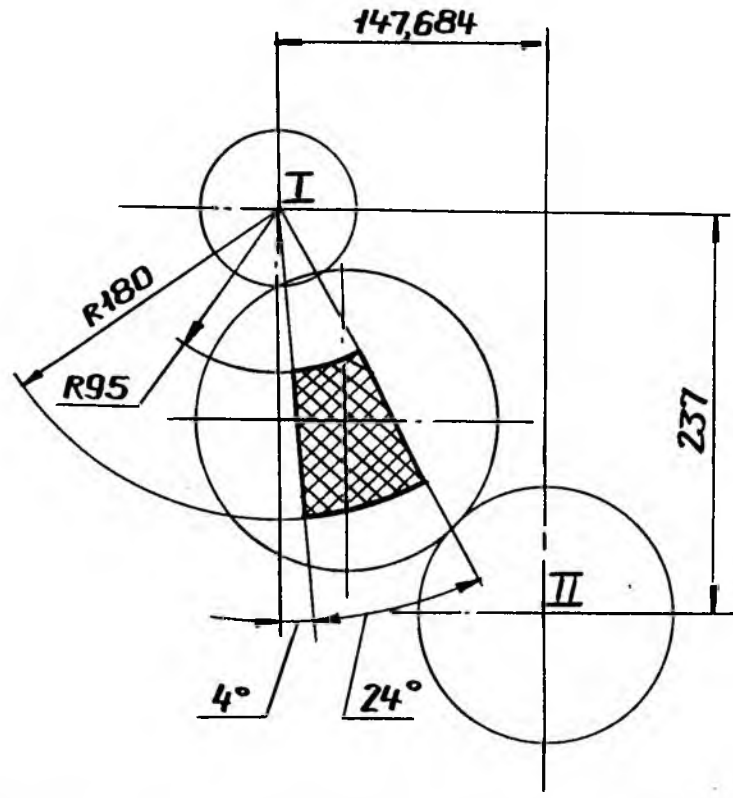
Чертеж для проверки возможности сцепления сменных зубчатых колес.
